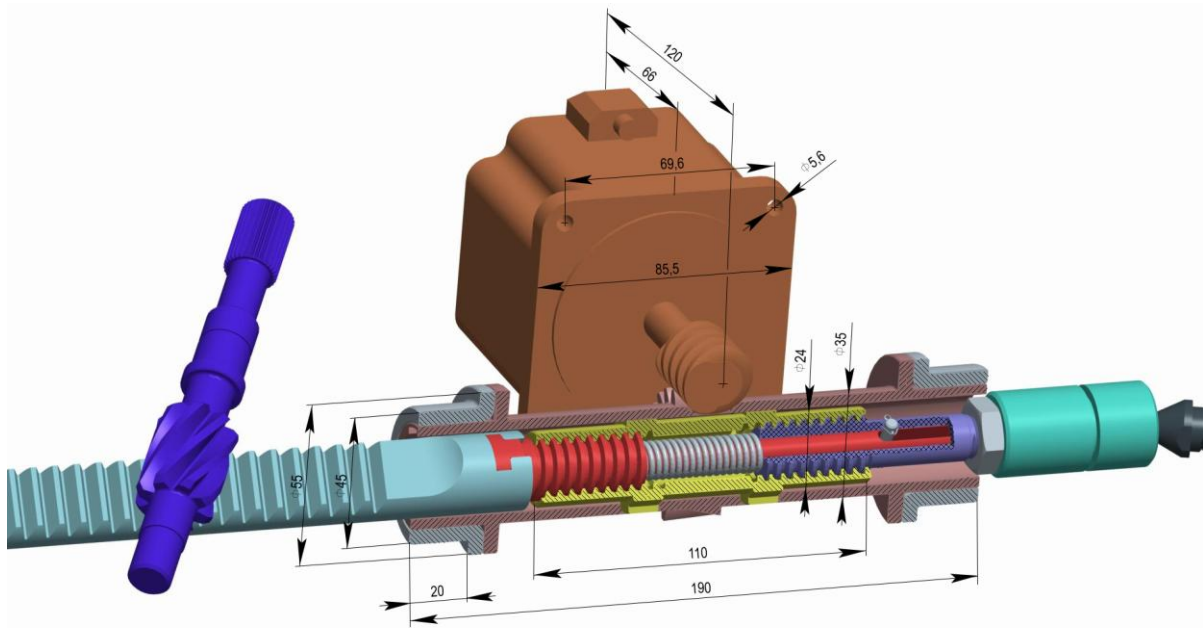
Základní rozměry krokového motoru SM 286-5255 [33]
